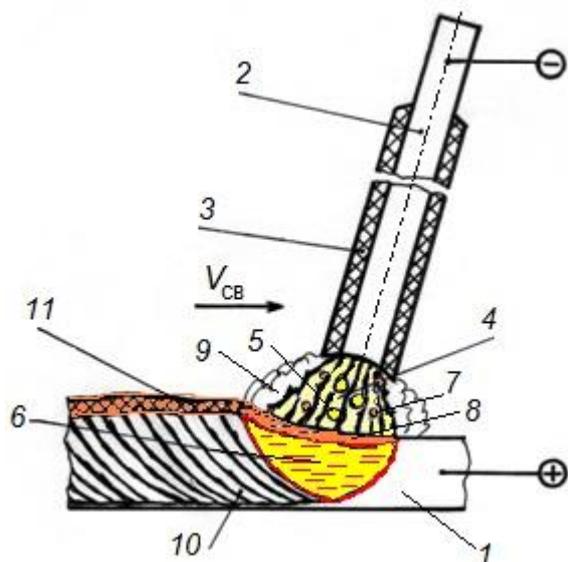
Схема процесса ручной дуговой сварки
